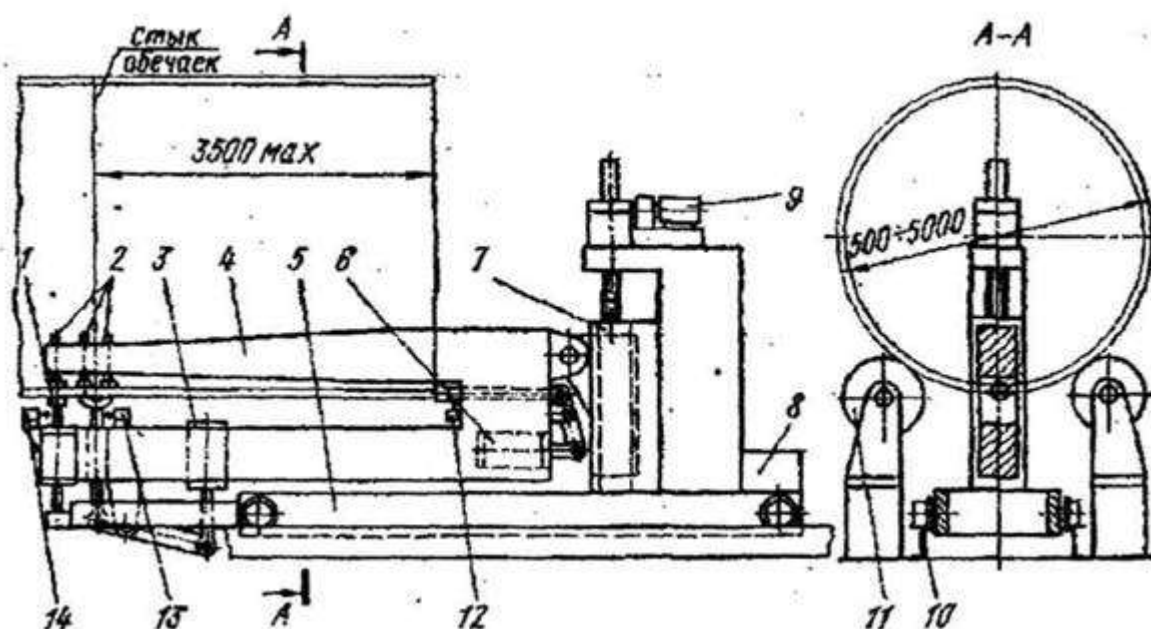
Установка для сборки обечайек по кольцевым стыкам
